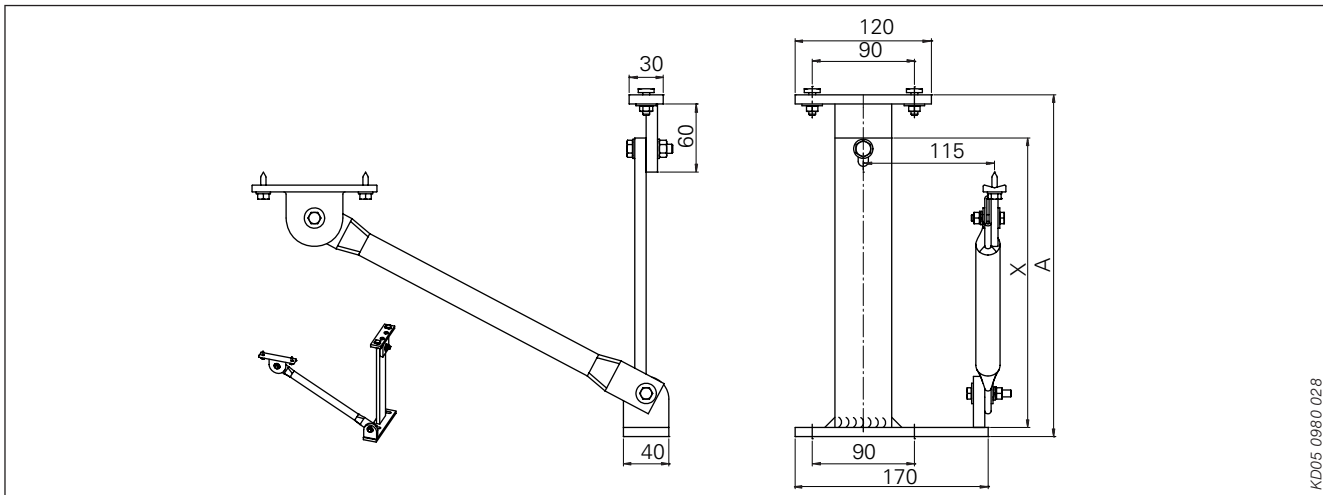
Soporte del carril guía nº 34 (soldado)
